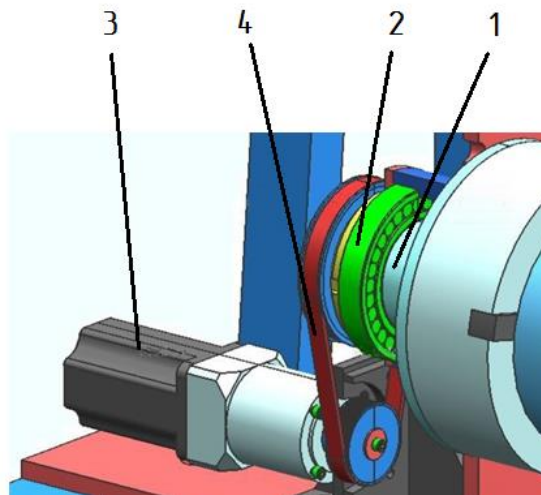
Схема приводу патрона механізму обертання труби
